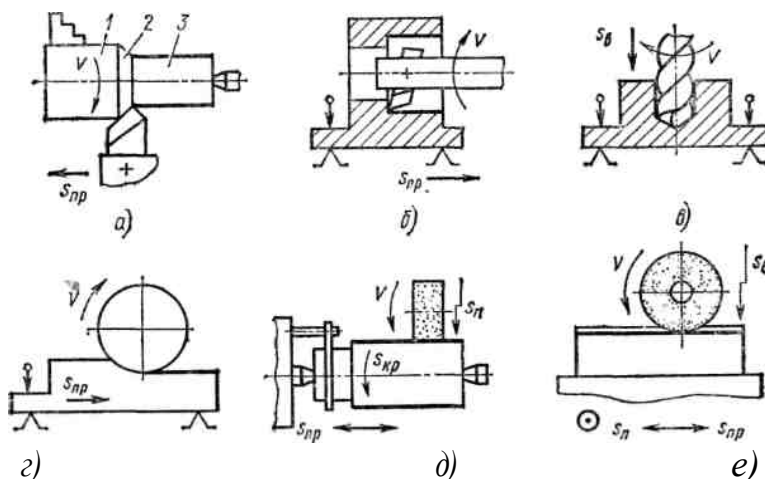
Элементы схем обработки и схемы обработки заготовок точением (а), растачиванием (б), сверлением (в), фрезерованием (г), шлифованием на кругло- (д) и плоскошлифовальных станках (е)
